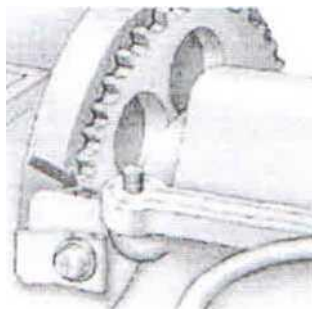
Установка поршня 1-го цилиндра в В.М.Т.
